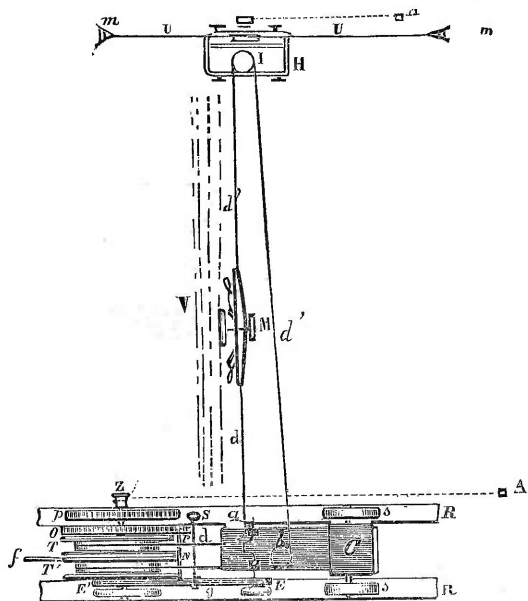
Vue en plan du treuil Boulet (Bajac).
